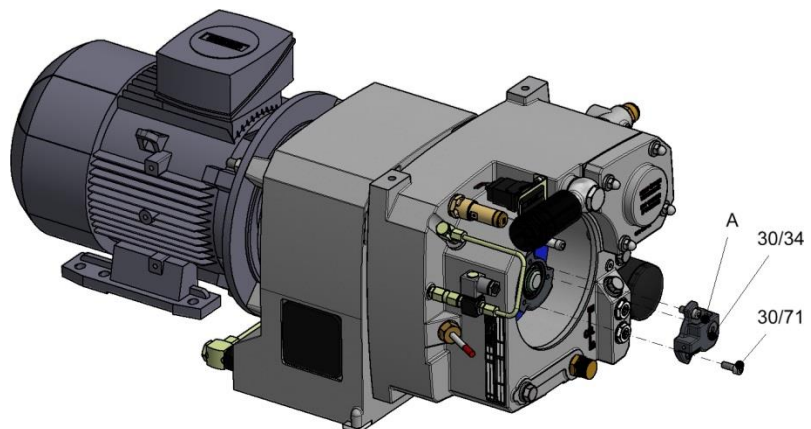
Démontez le couvercle du régulateur (pos. 30/34)
